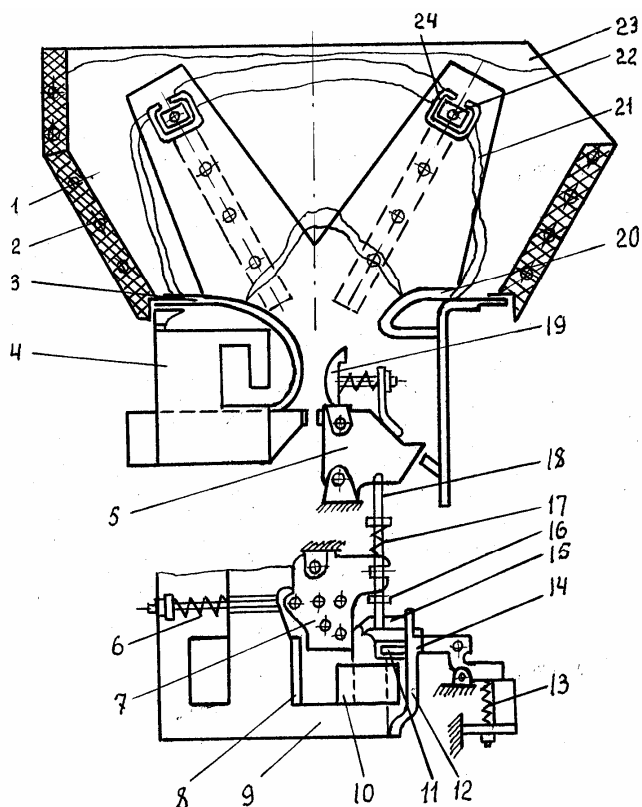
Дополнительная камера выключателя ВАТ-42: 1 –дугогасительная камера; 2 – торцовые вставки; 3,20,24 – электроды (рога); 4 – главный неподвижный контакт; 5 – главный подвижный контакт; 6 – отключающая пружина; 7,11 – якорь; 8,15 – упор; 9 – магнитопровод; 10 – катушка; 12 – магнитопроводящая скоба; 13 – пружина; 14 – защёлка; 16 – рычаг; 17 – возвратная пружина; 18 – тяга; 19 – дугогасительный контакт; 21 – перегородки; 22 – П-образный магнитопровод; 23 – щиты
